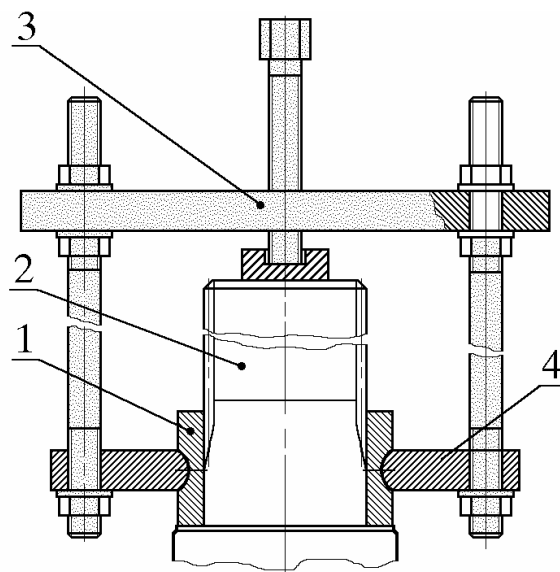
а. Выпрессовка внутренней обоймы подшипника промежуточной опоры с промежуточного вала:
